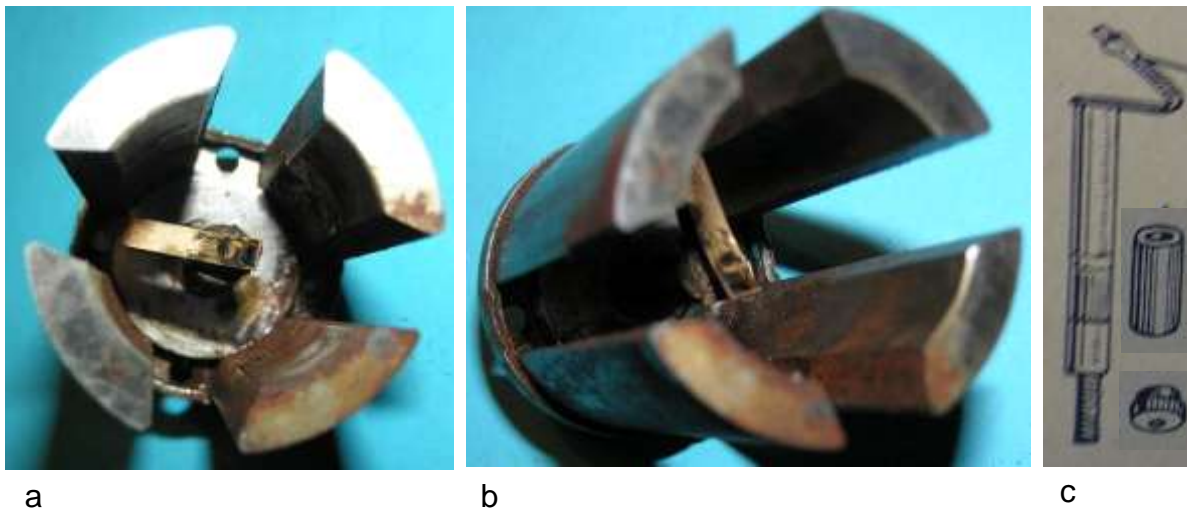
Blattfeder mit Kabelbolzen: a) Kontaktfläche der Blattfeder, b) Axialer Bewegungsfreiraum der Blattfeder, c) Kabelbolzen mit Blattfeder, Isolierhülse und Rändelmutter
